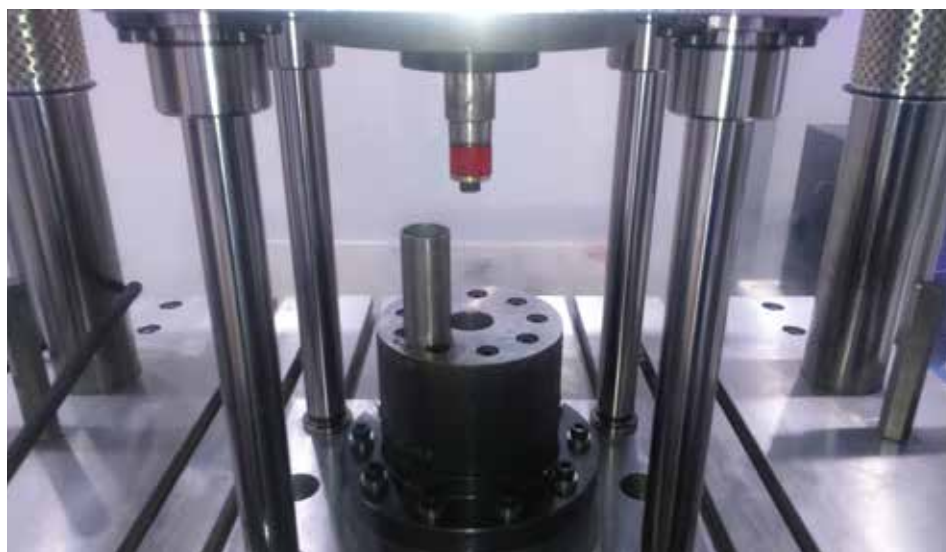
Blockeinheit mit eingebauter Prüfvorrichtung und Prüfling
